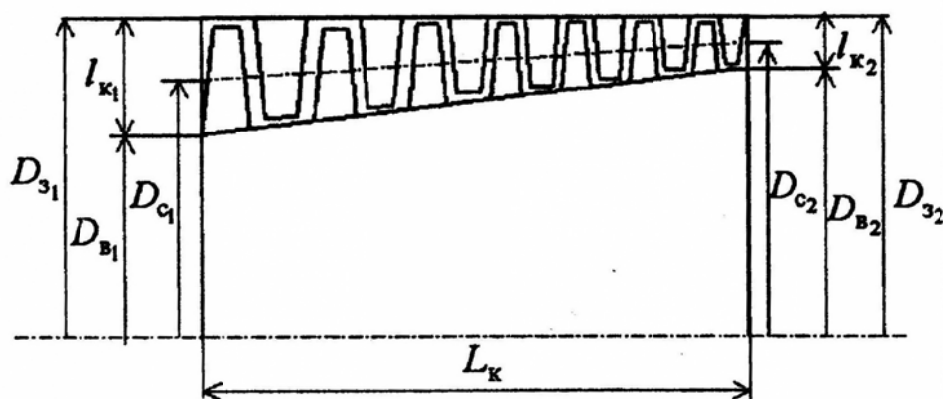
Меридіанний переріз проточної частини компресорів ГТД
